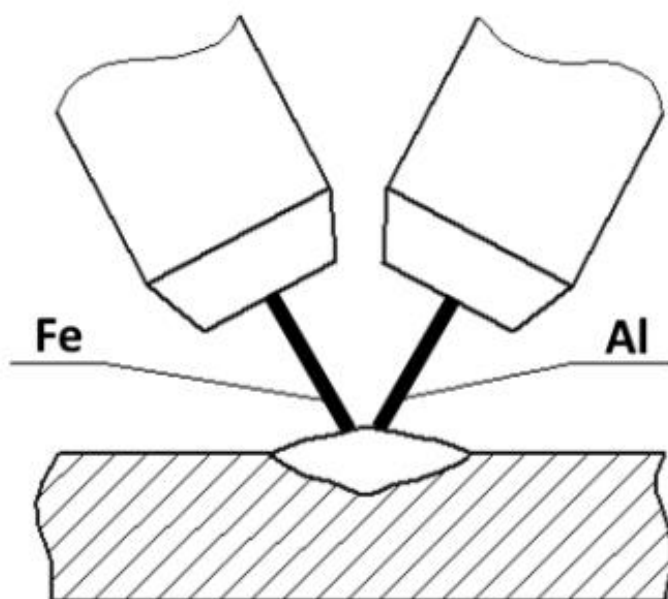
Схематичное изображение двухдуговой наплавки
